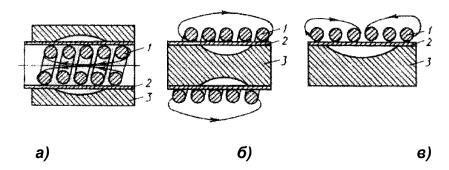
Основные схемы электромагнитной штамповки: а — раздача трубчатой заготовки; б— обжим трубчатой заготовки; в — формовка, неглубокая вытяжка листовой заготовки; 1 — индуктор; 2 — заготовка; 3 — матрица (оправка)
